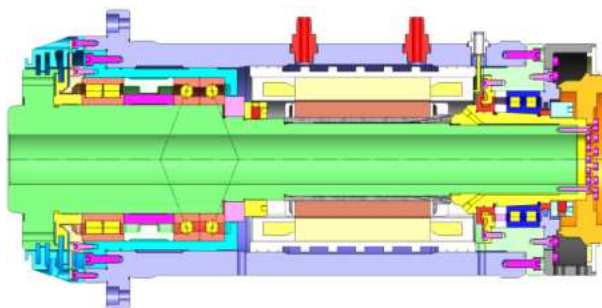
AP pentru strung CNC cu motor incorporat și lagăr conducător format din rulment dublu cu role cilindrice și un set DB de rulmenți cu contact unghiular
